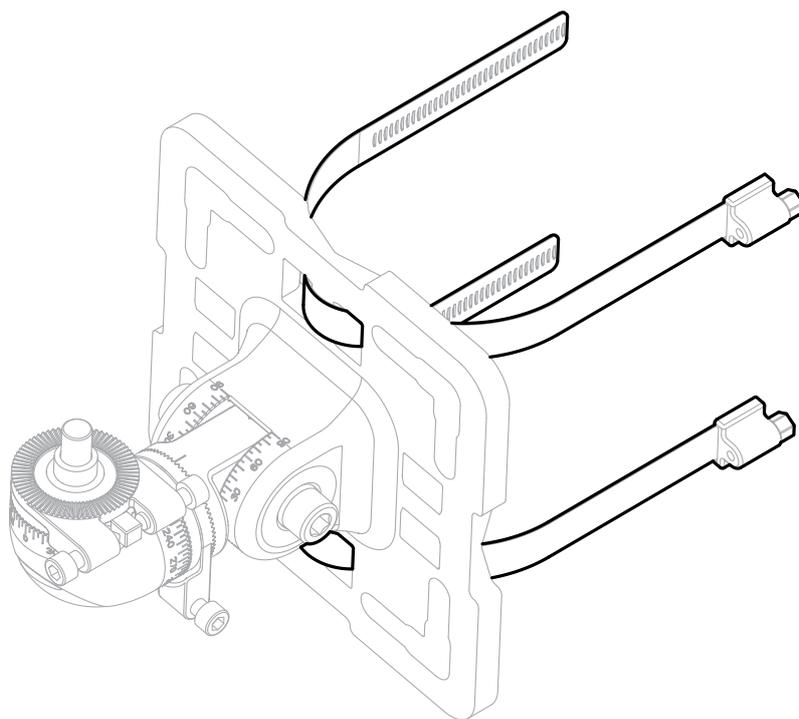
Encaixe do suporte de montagem universal com abraçadeiras
